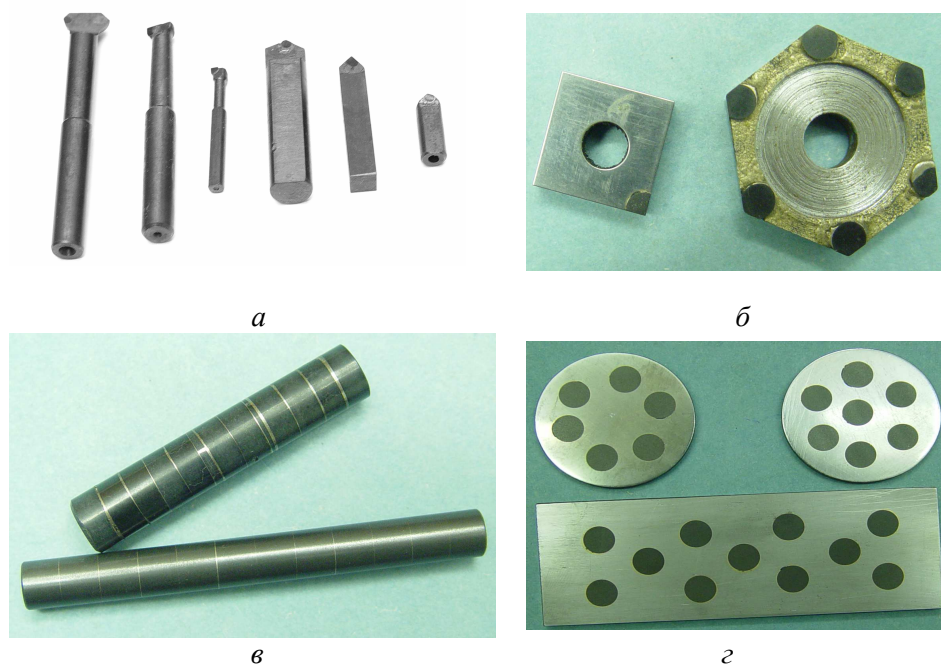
Паяные изделия инструментального и конструкционного назначений на основе BN_{cf} : а — резцы; б — пластины; в — эльборовые стержни; г — подпятники опор подшипников скольжения
